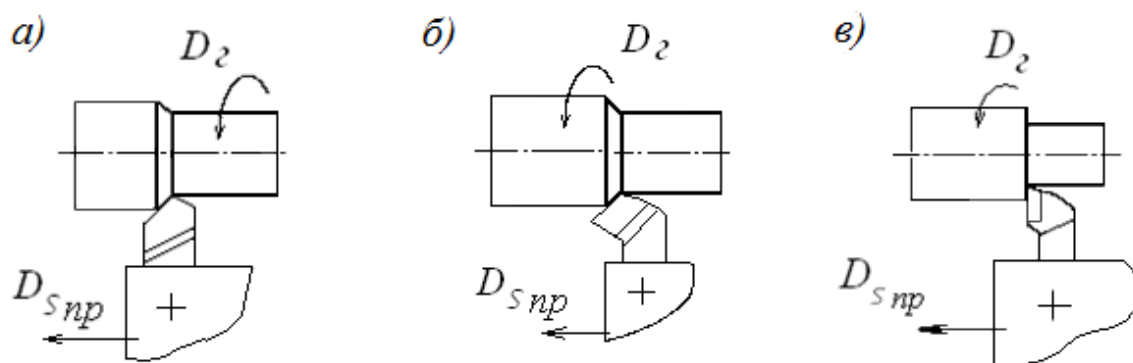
Схемы точения наружной цилиндрической поверхности:
